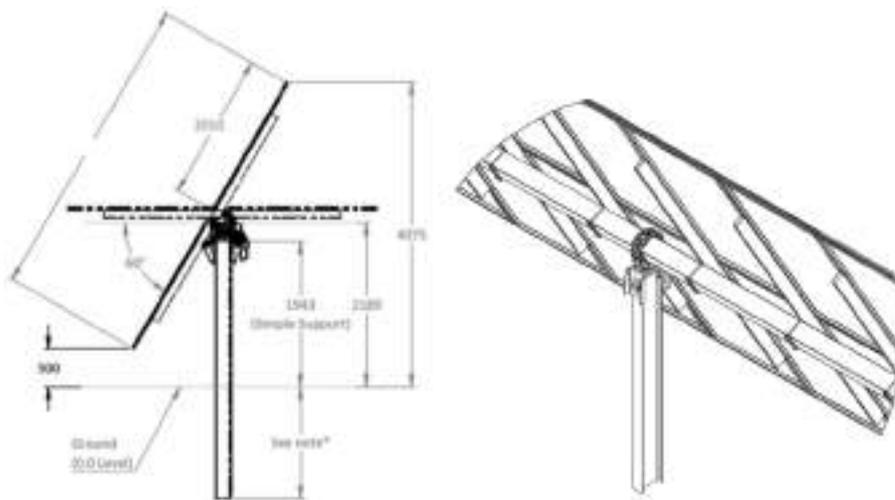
Perfil Seguidor Soltec y detalle eje
